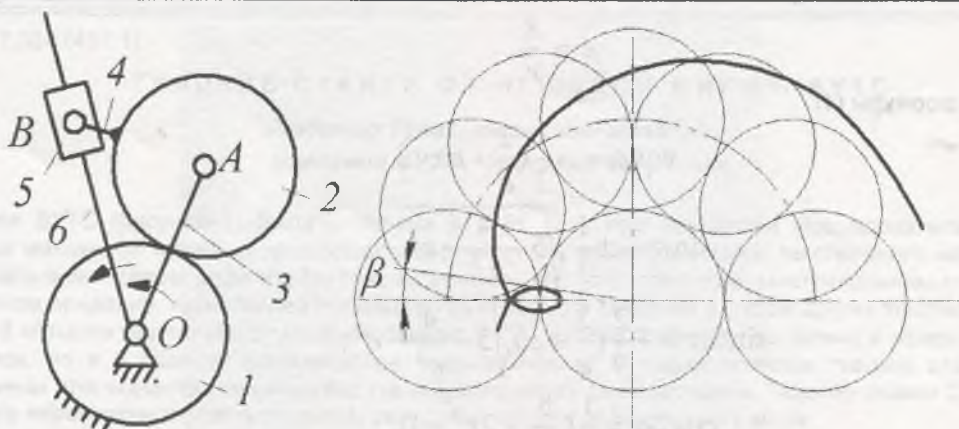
Кинематическая схема механизма с квазиостановками и траектория движения ведомого шарнира
